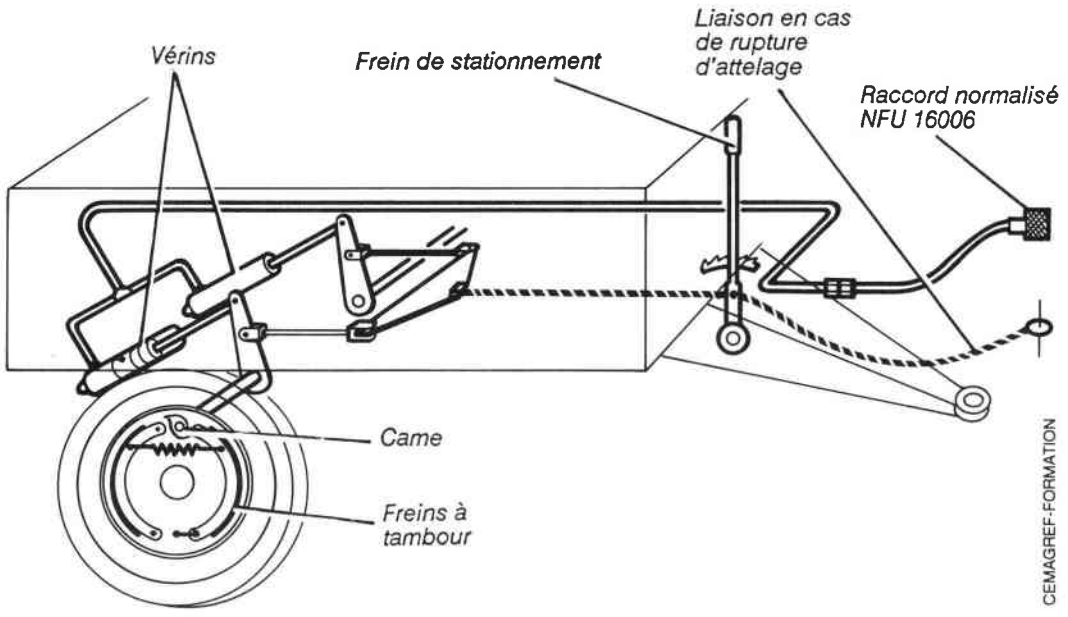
Le principe du freinage hydraulique d'une remorque.
